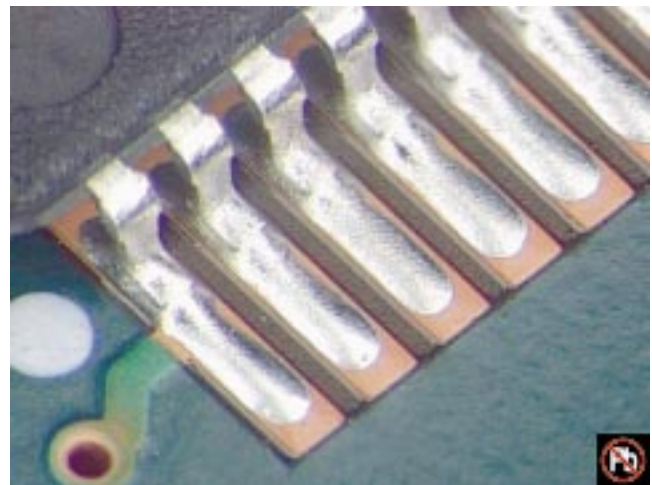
Soldadura SnAgCu; Flux Soluble en Agua
